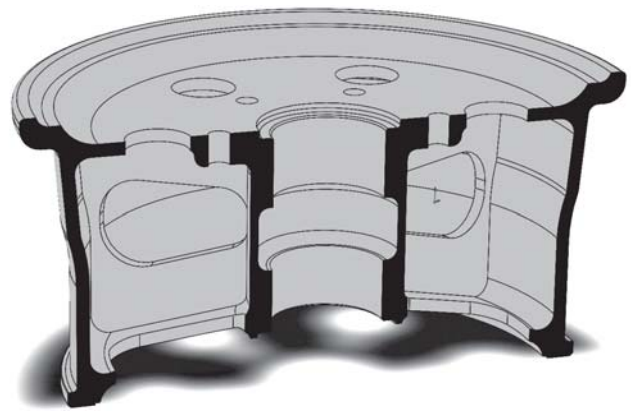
3D-модель заготовки (в разрезе) после операции сверления отверстий
